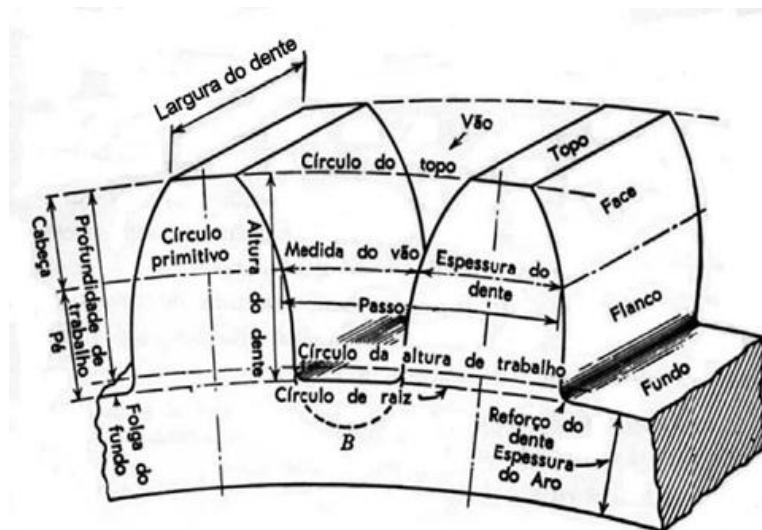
Engrenagens-Cilíndricas de Dentes Retos
